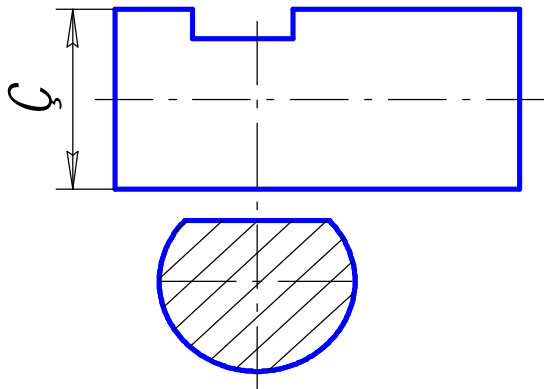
Чертеж фрагмента вала с прямоугольным пазом.
